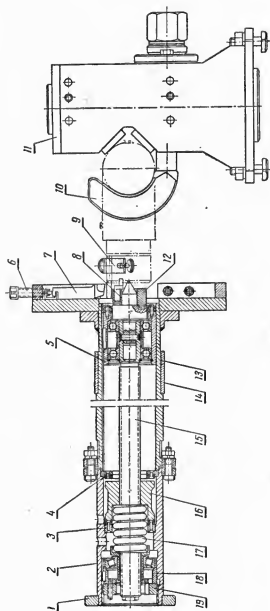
Приспособление для обточки коленообразных осей на токарном станке:
